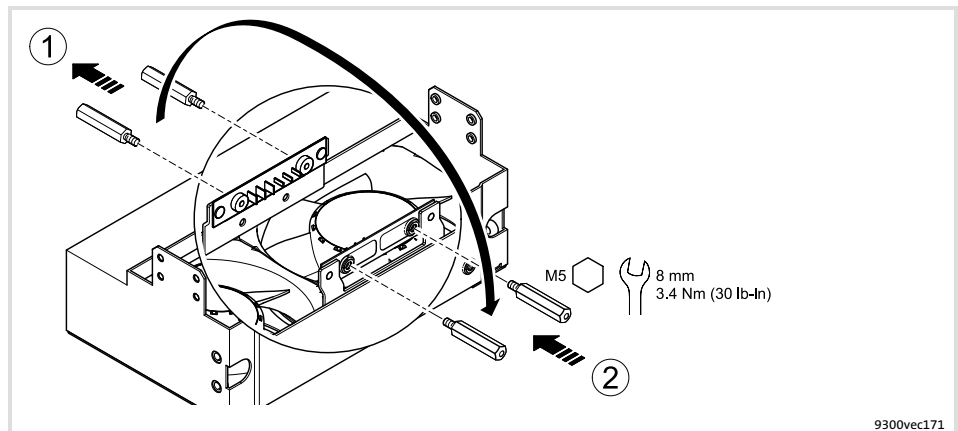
Gewindehülsen für die Spannungsversorgung der Lüfter umbauen
